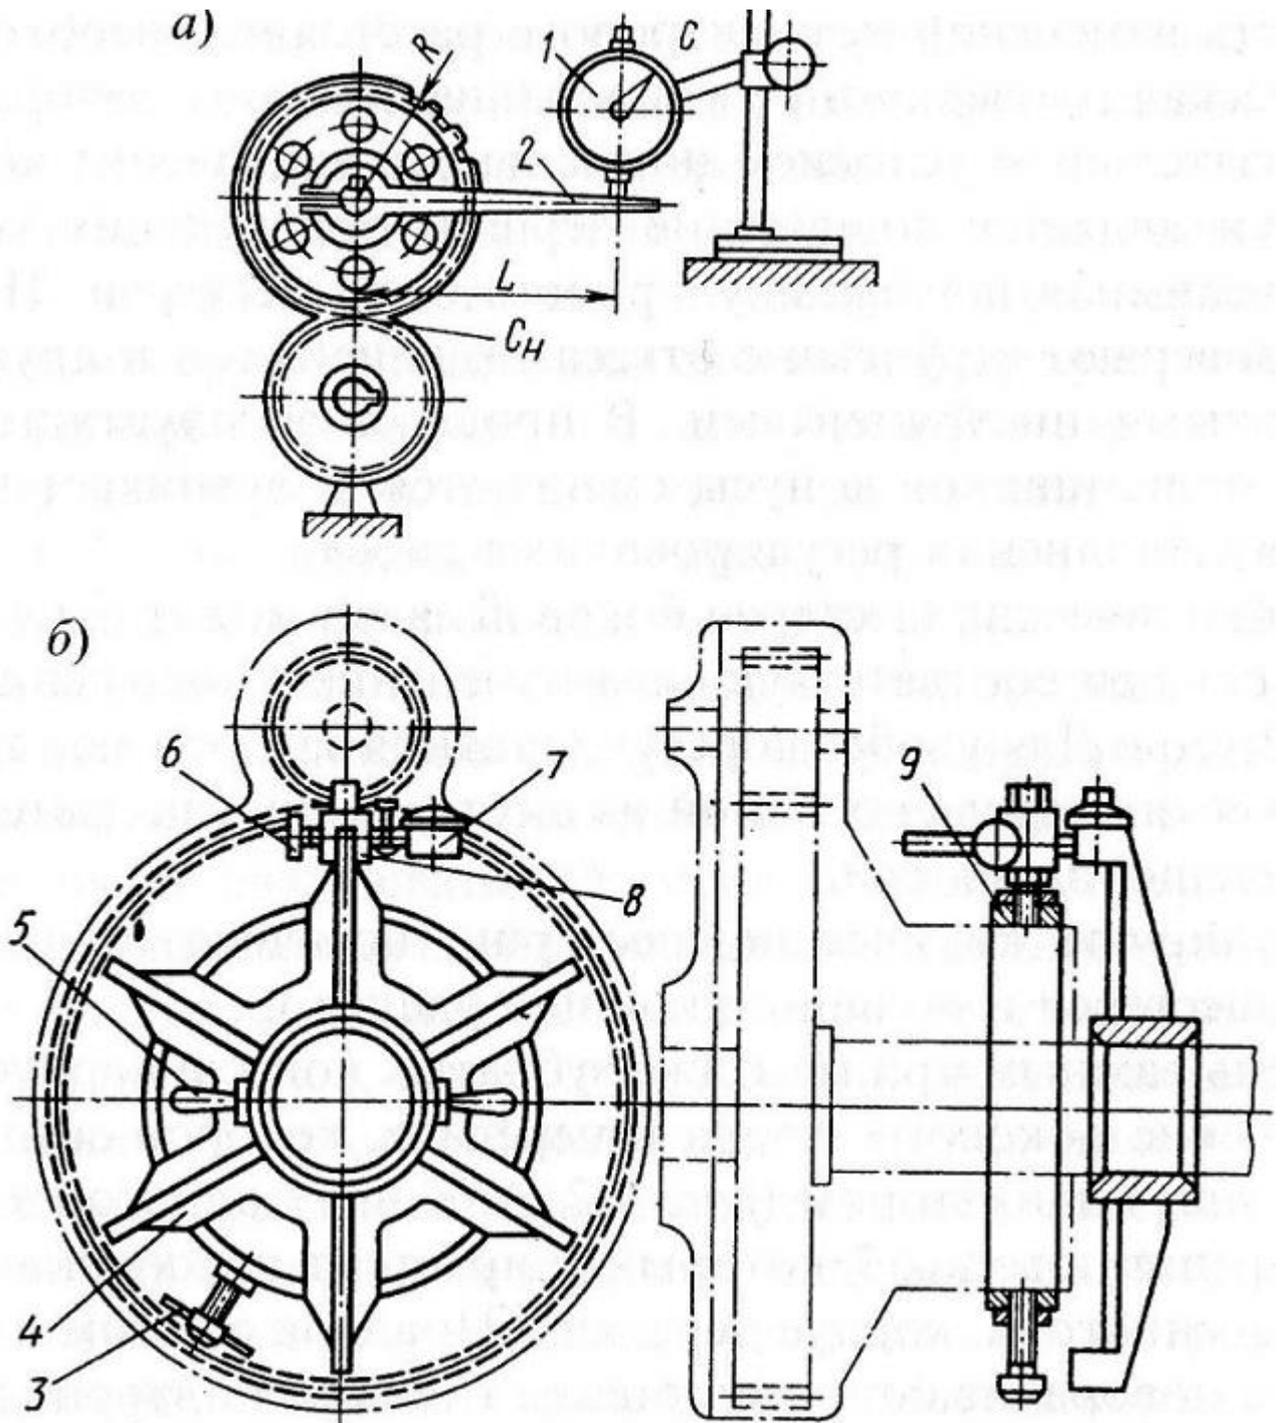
Способы измерения бокового зазора в цилиндрической зубчатой передаче при открытом (а) и закрытом (б) доступе к ней: 1,7 – индикаторы; 2 – поводок; 3,6 – винты; 5 – рукоятка; 8 – стойка; 9 - хомутик
